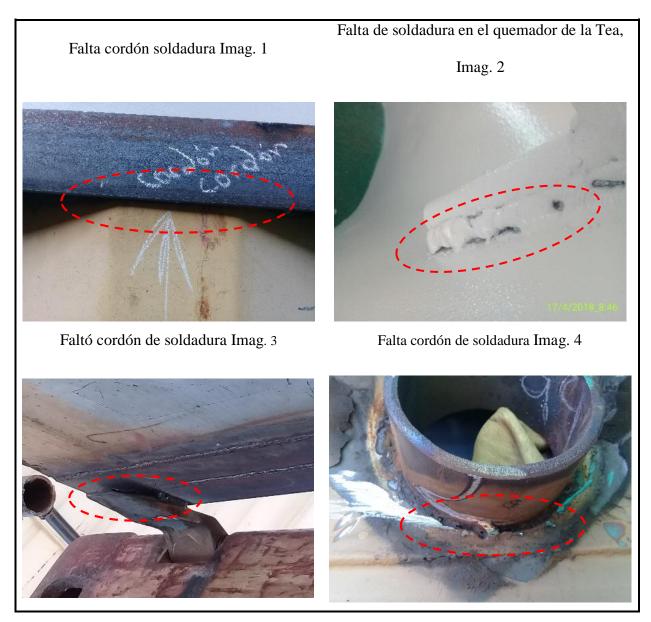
Inspección en el área de soldadura. (1 parte)
